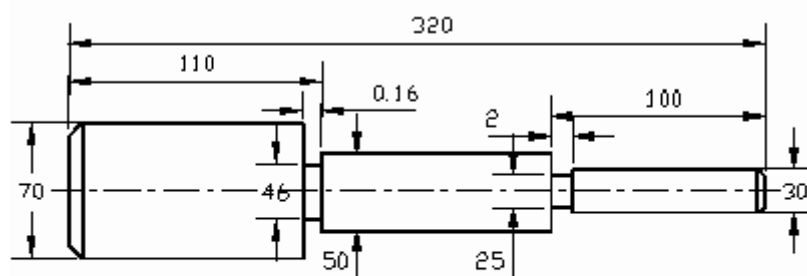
Типовая обрабатываемая деталь - ступенчатый вал
